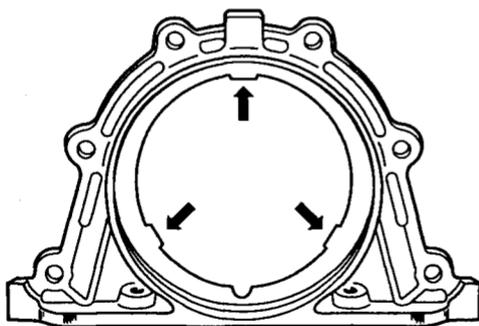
Держатель заднего сальника коленчатого вала (стрелками показаны выступы для центрирования держателя относительно фланца коленчатого вала)
